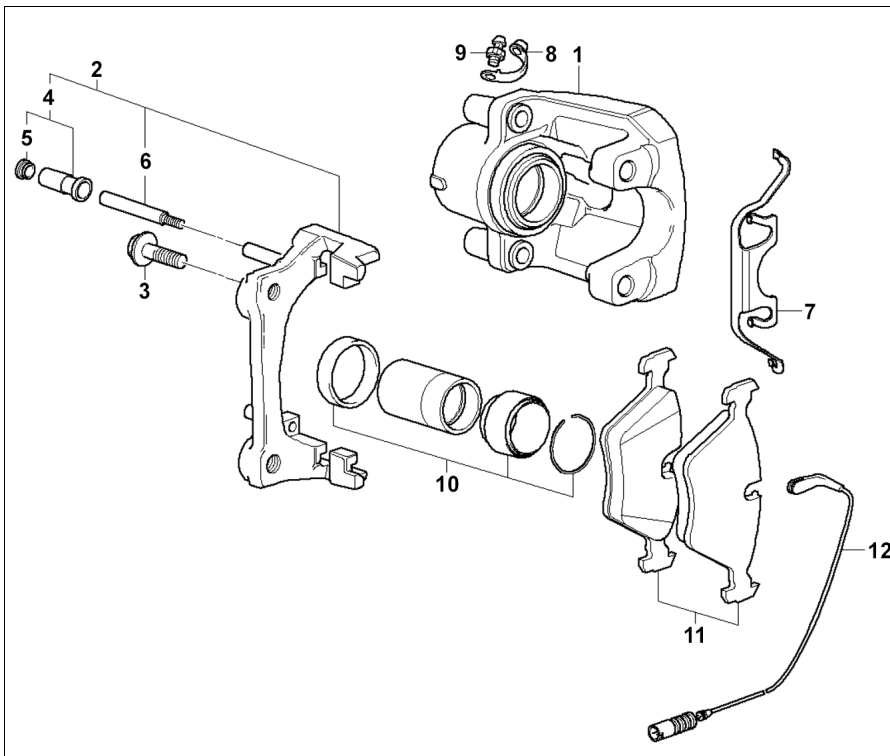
Тормозной механизм задних колес. 1 - корпус суппорта, 2 - направляющая тормозных колодок, 3 - болт (M10x26,5), 4 - направляющая втулка, 5 - пробка, 6 - направляющий палец, 7 - фиксирующая пружина, 8 - пылезащитный колпачок, 9 - штуцер прокачки, 10 - уплотнители, 11 - тормозные колодки, 12 - датчик износа.
